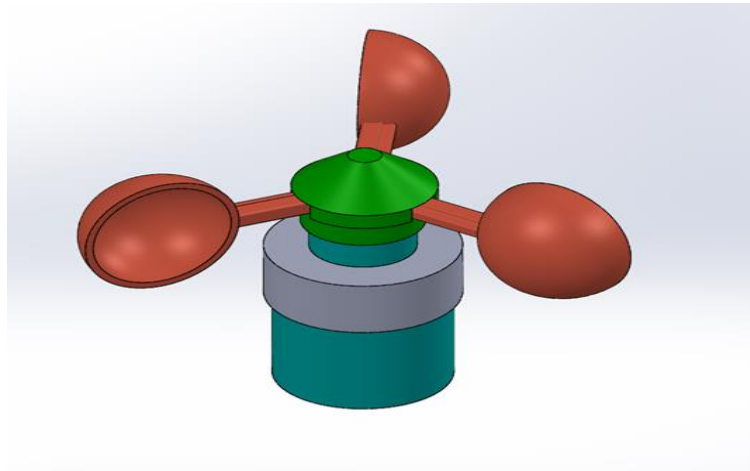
Vue tridimensionnelle de l'anémomètre modélisé avec SolidWorks
